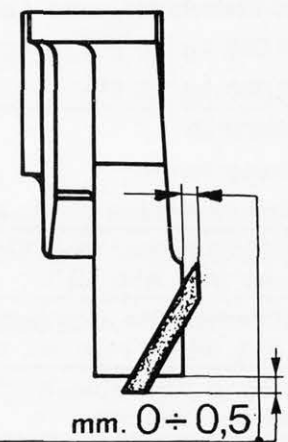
Befestigung der Dichtungen auf den Hauptlagern.
